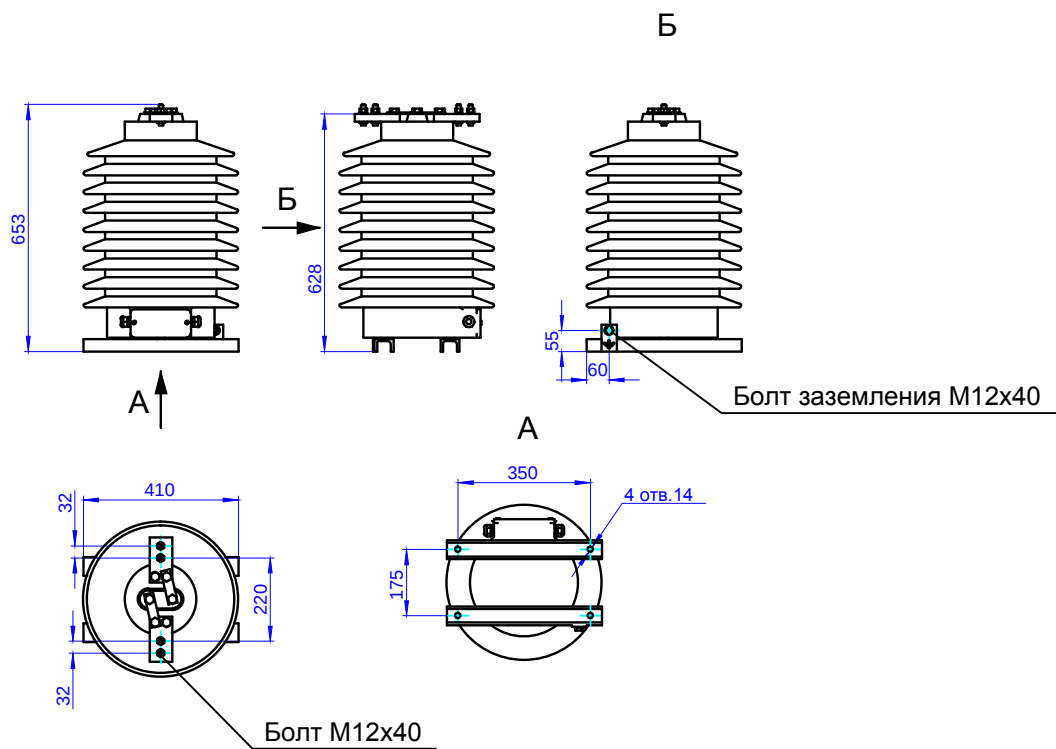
Габаритный чертеж трансформатора тока небаланса
